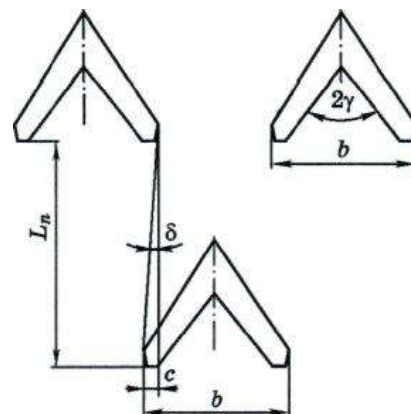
Схема розміщення поліельних лап з перекриттям
